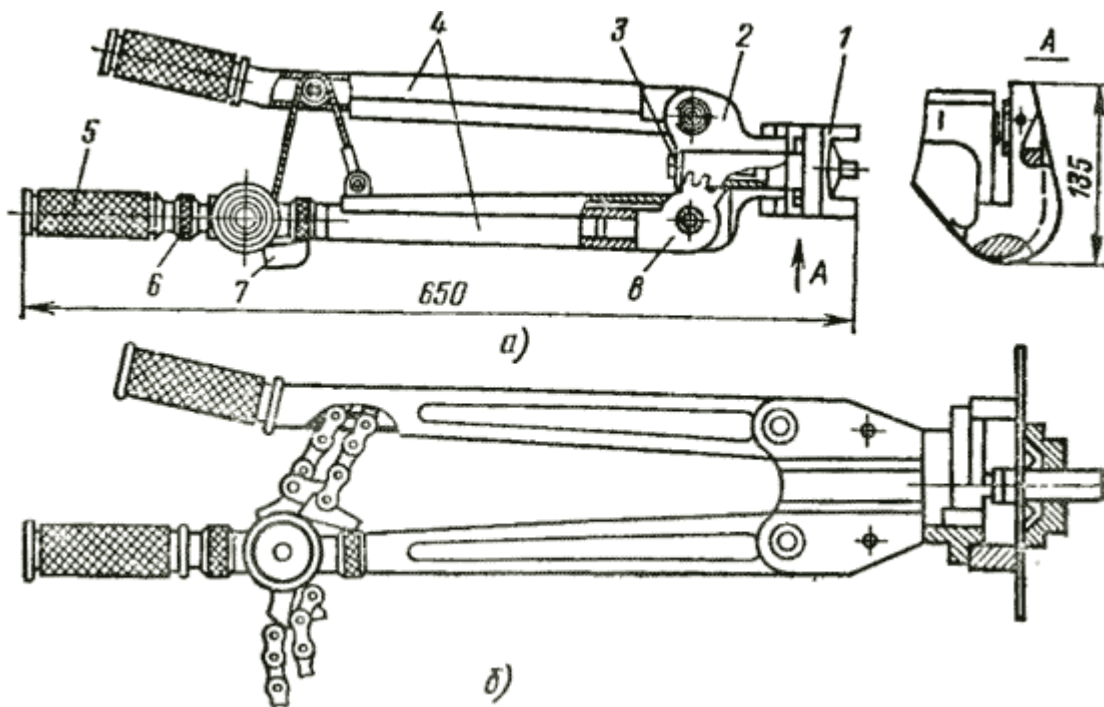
Ручные механические прессы для пробивки отверстий; а - ПРМПО; б - РППО-3
